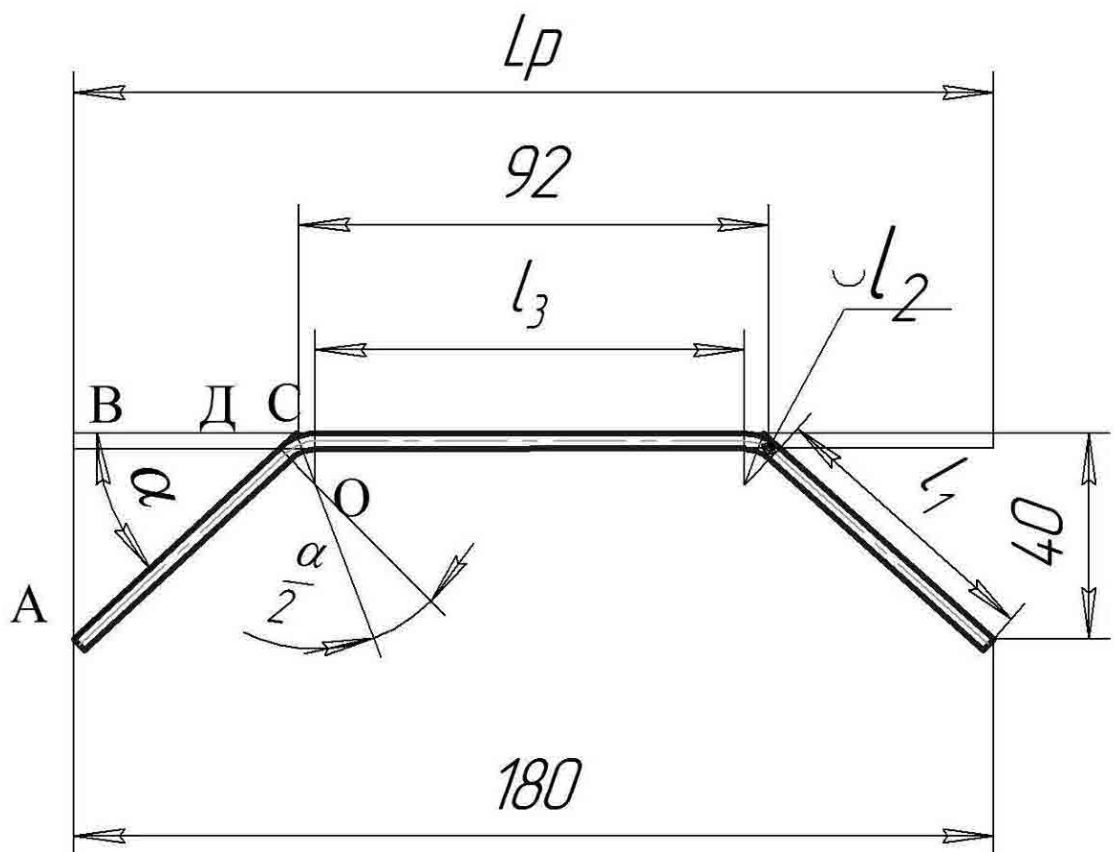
До розрахунку довжини розгортки l_p вихідної заготовки
